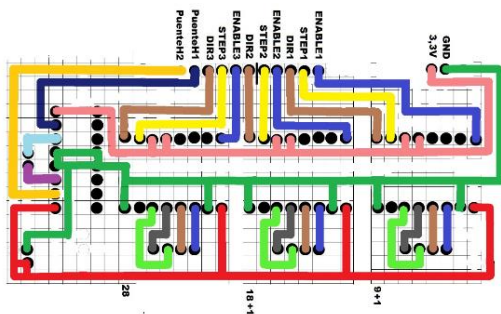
Caminos de soldadura que fueron realizados en la perfboard.
